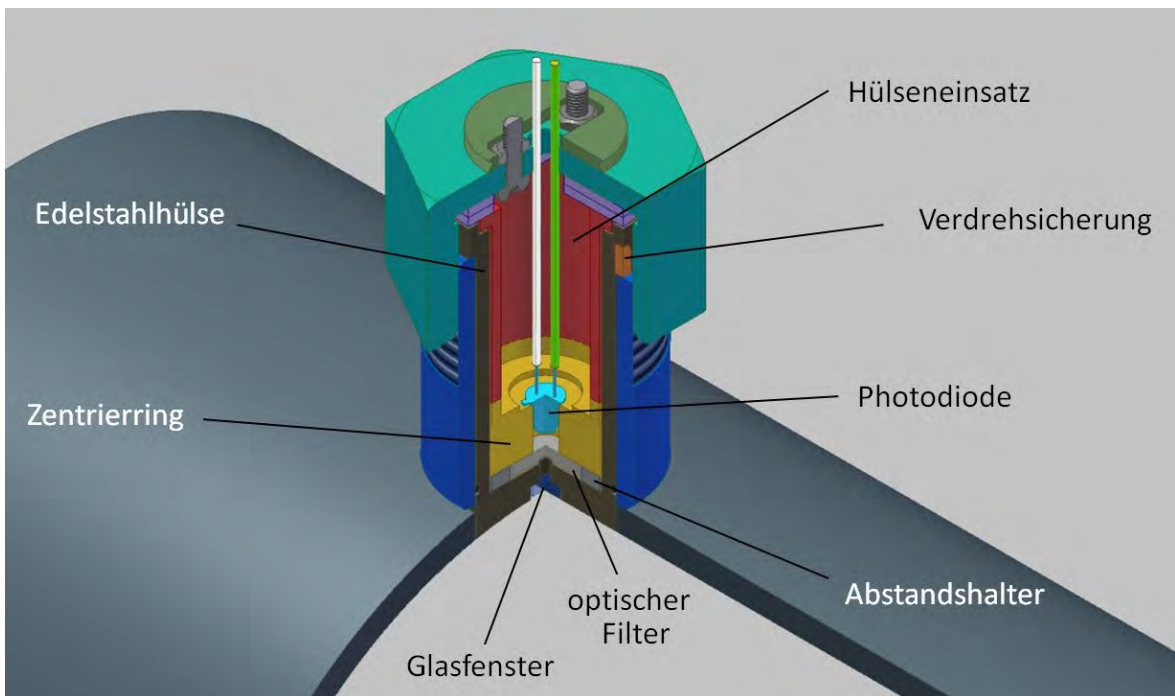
CAD-Konstruktion des neuen Flammensensors mit optimierter Befestigung.
